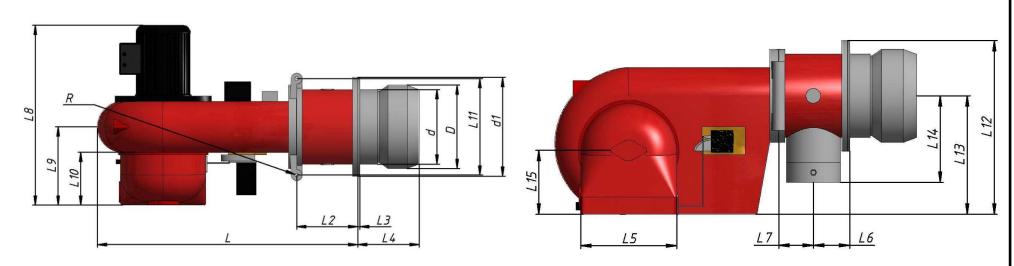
Габаритные и присоединительные размеры горелок ГГБ-0,63...ГГБ-4,1
